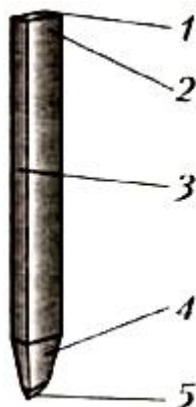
Зубило: 1 - головка; 2 — ударная часть; 3 — стержень; 4 - рабочая часть; 5 — режущая кромка
